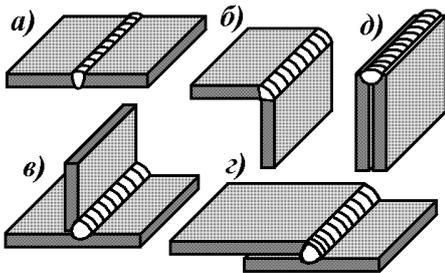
Типы сварных соединений: а) стыковое; б) угловое; в) тавровое; г) нахлесточное; д) торцовое
